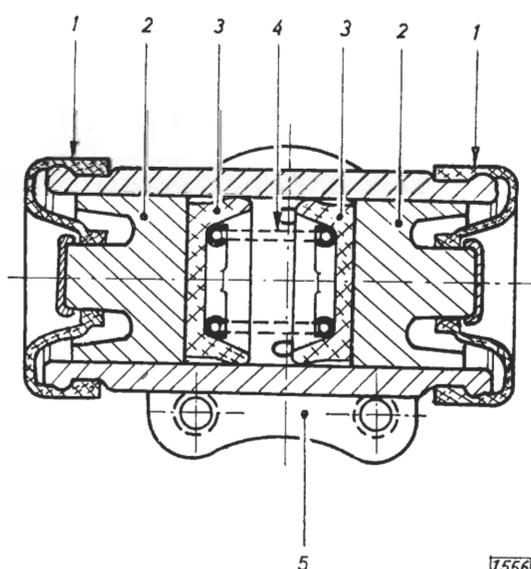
Zweiseitig wirkender Bremszylinder für Vorderradbremse
